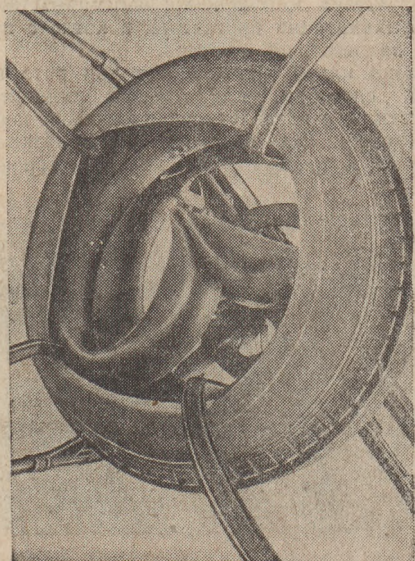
Закладка варочной камеры с помощью расширителя бортов.
